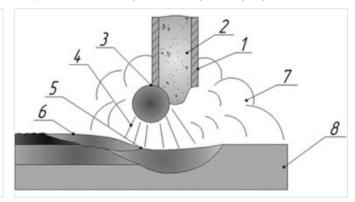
Схема процесса сварки самозащитной порошковой проволокой. 1— стальная оболочка, 2— порошковый сердечник, 3— капля металла, 4— электрическая дуга, 5— сварочная ванна, 6— шлак, 7— образующийся защитный газ, 8— свариваемая (наплавляемая) поверхность
